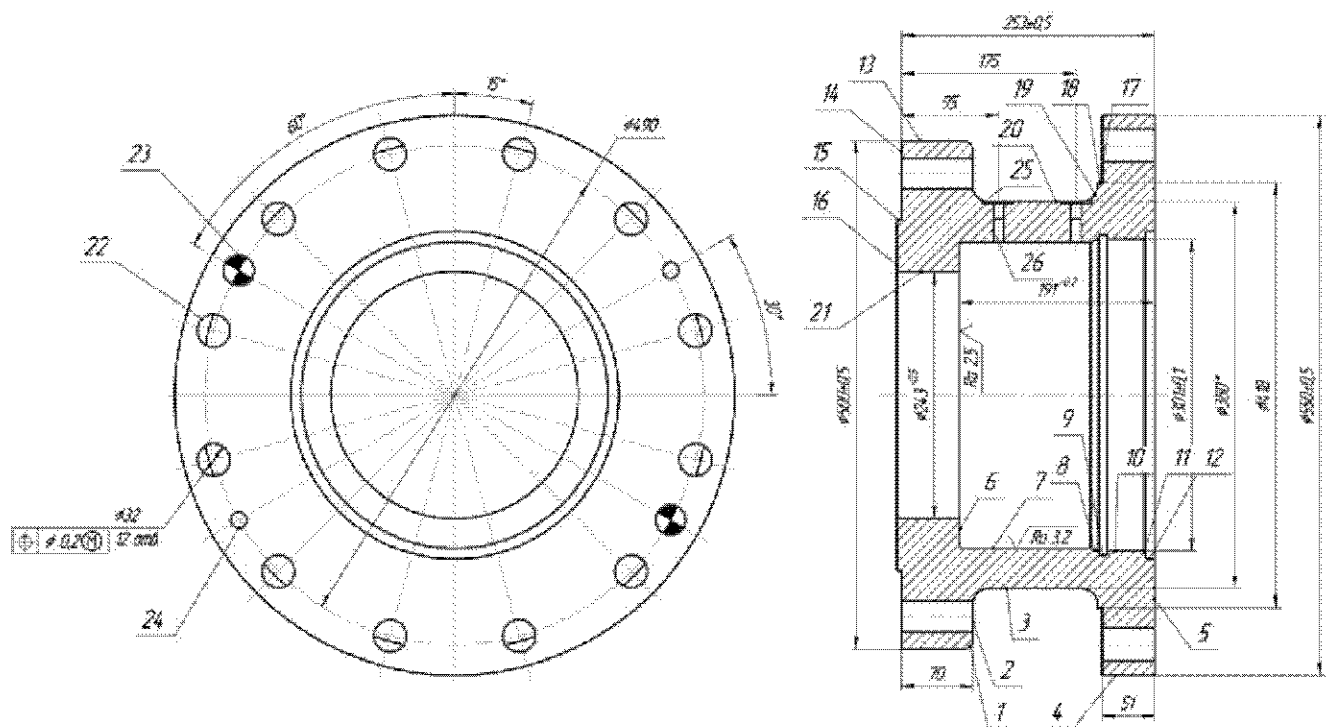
Эскиз детали «Корпус бугельного узла»
